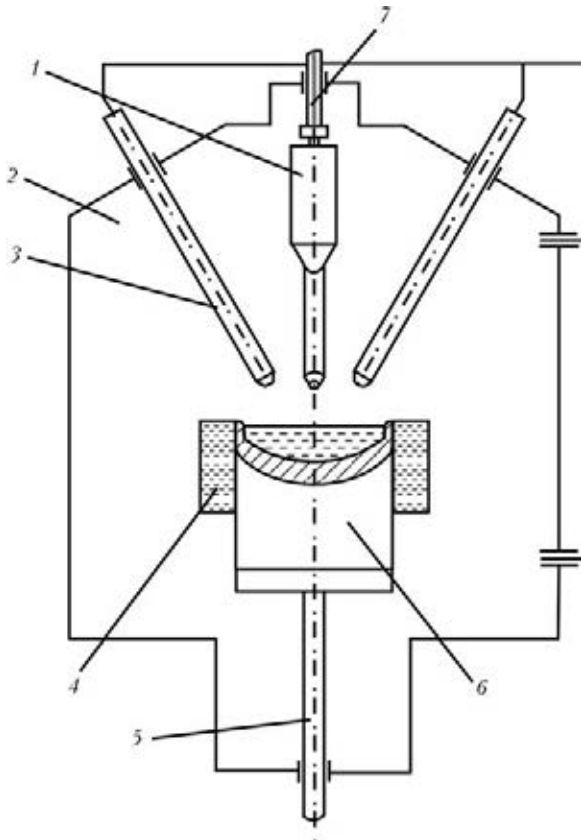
Схема плазменно-дуговой печи УПП-3: 1 — заготовка; 2 — камера; 3 — плазмотрон; 4 — кристаллизатор; 5 — механизм вытягивания слитка; 6 — слиток; 7 — механизм подачи заготовки
